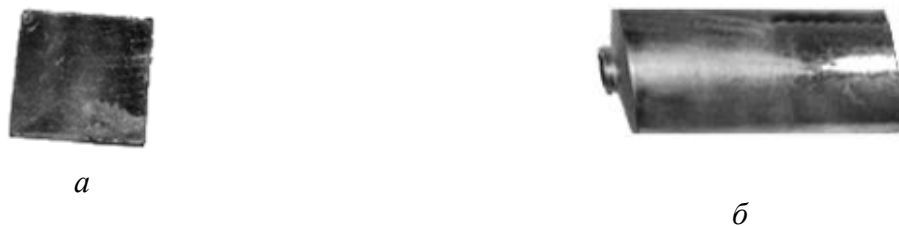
Схема процесу видавлювання тюбика з квадратної заготовки за два переходи:
